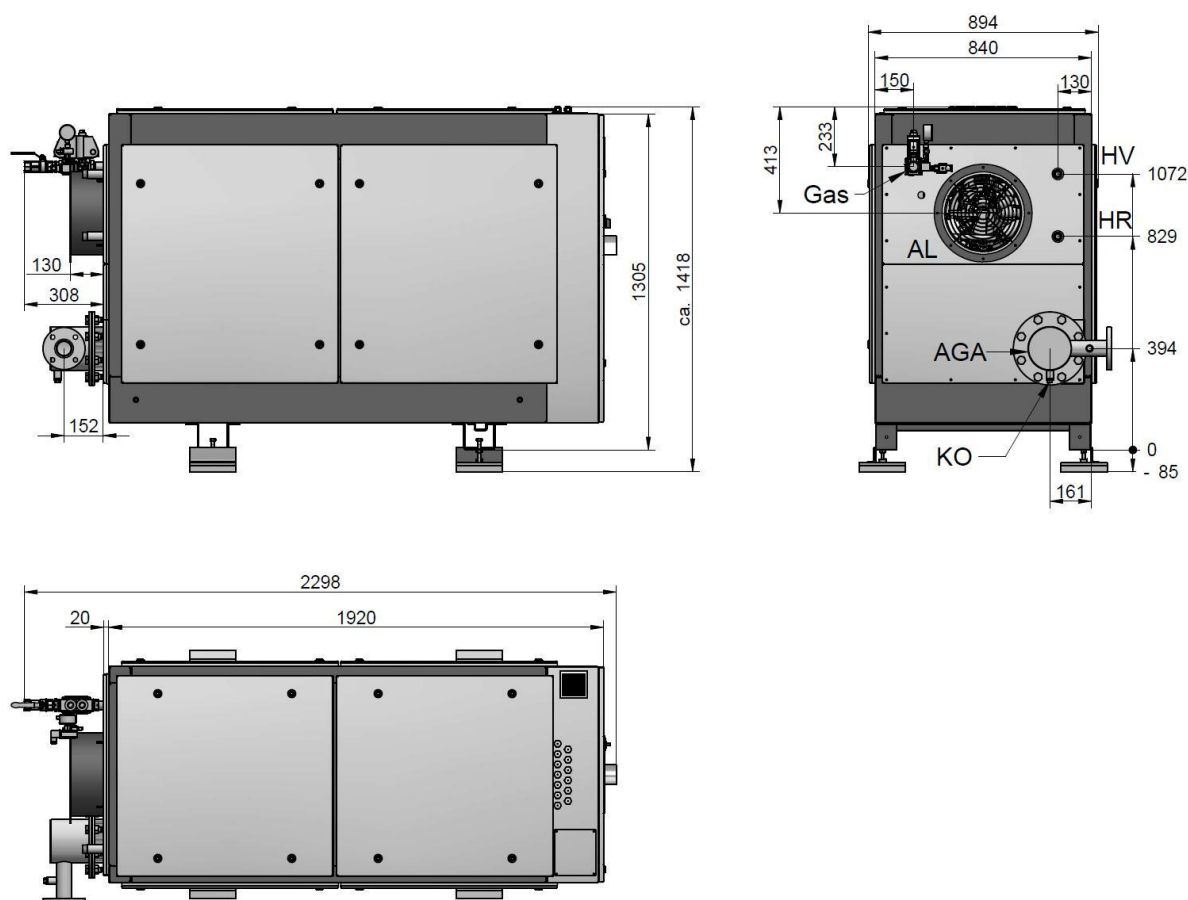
Abmessungen und Anschlüsse der BHKW Module Vitobloc 200 EM-20/39 (Maße in mm)
